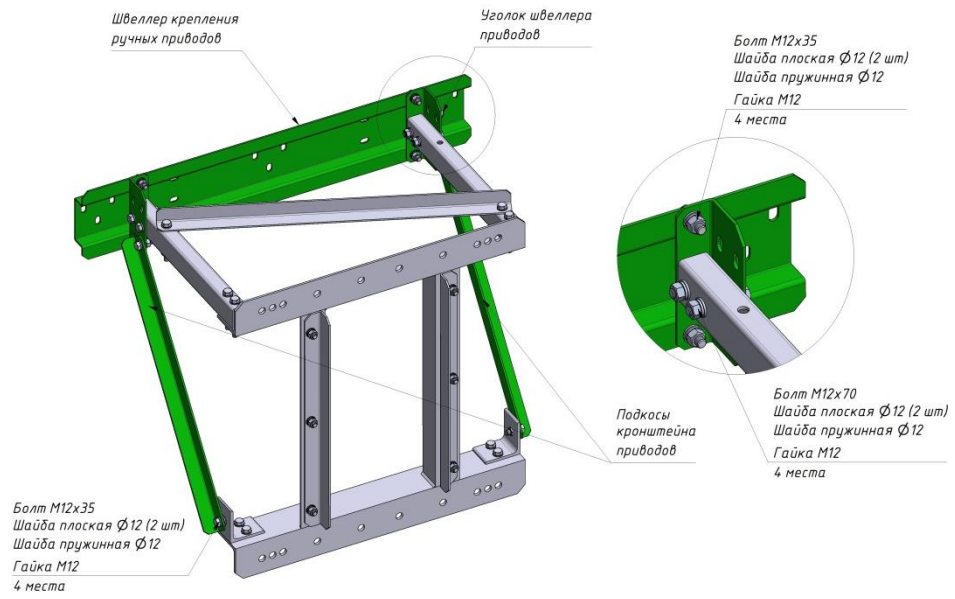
Установка швеллеров для крепления приводов разъединителя
